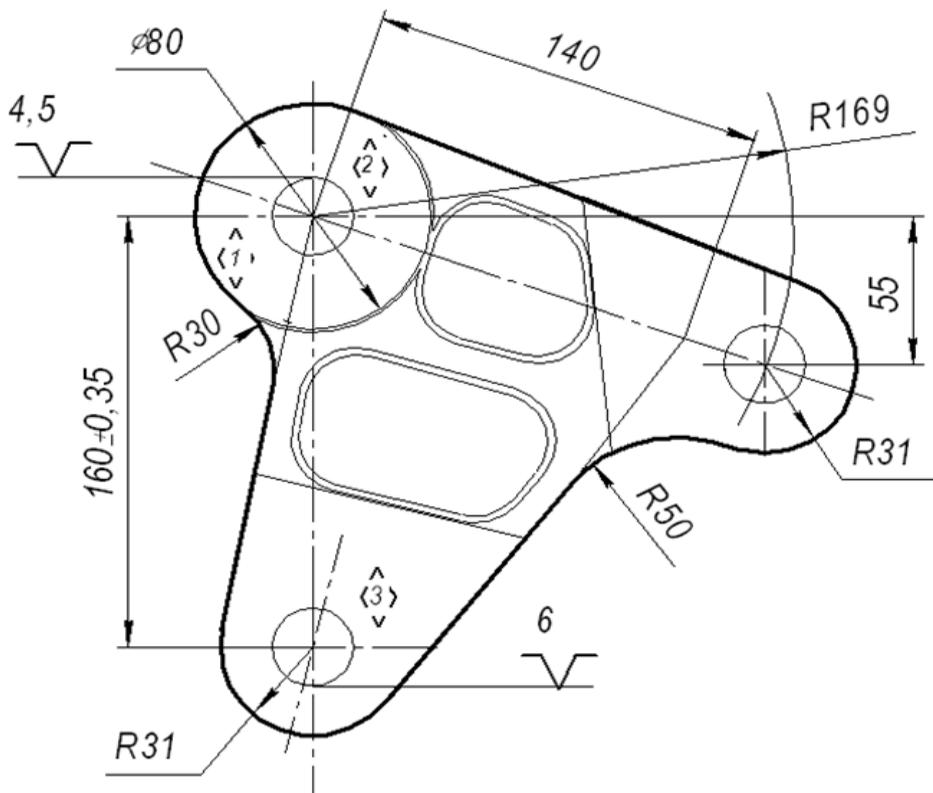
Эскиз обработки детали типа «Кронштейн»
